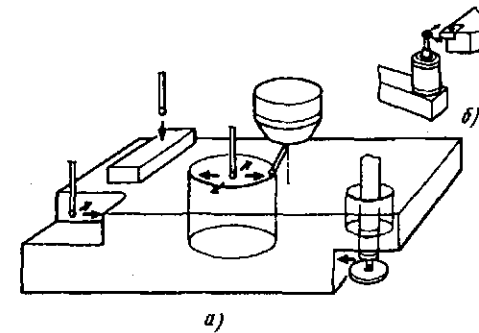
Схемы измерений обрабатываемой детали (а) и режущего инструмента (б) щупами
